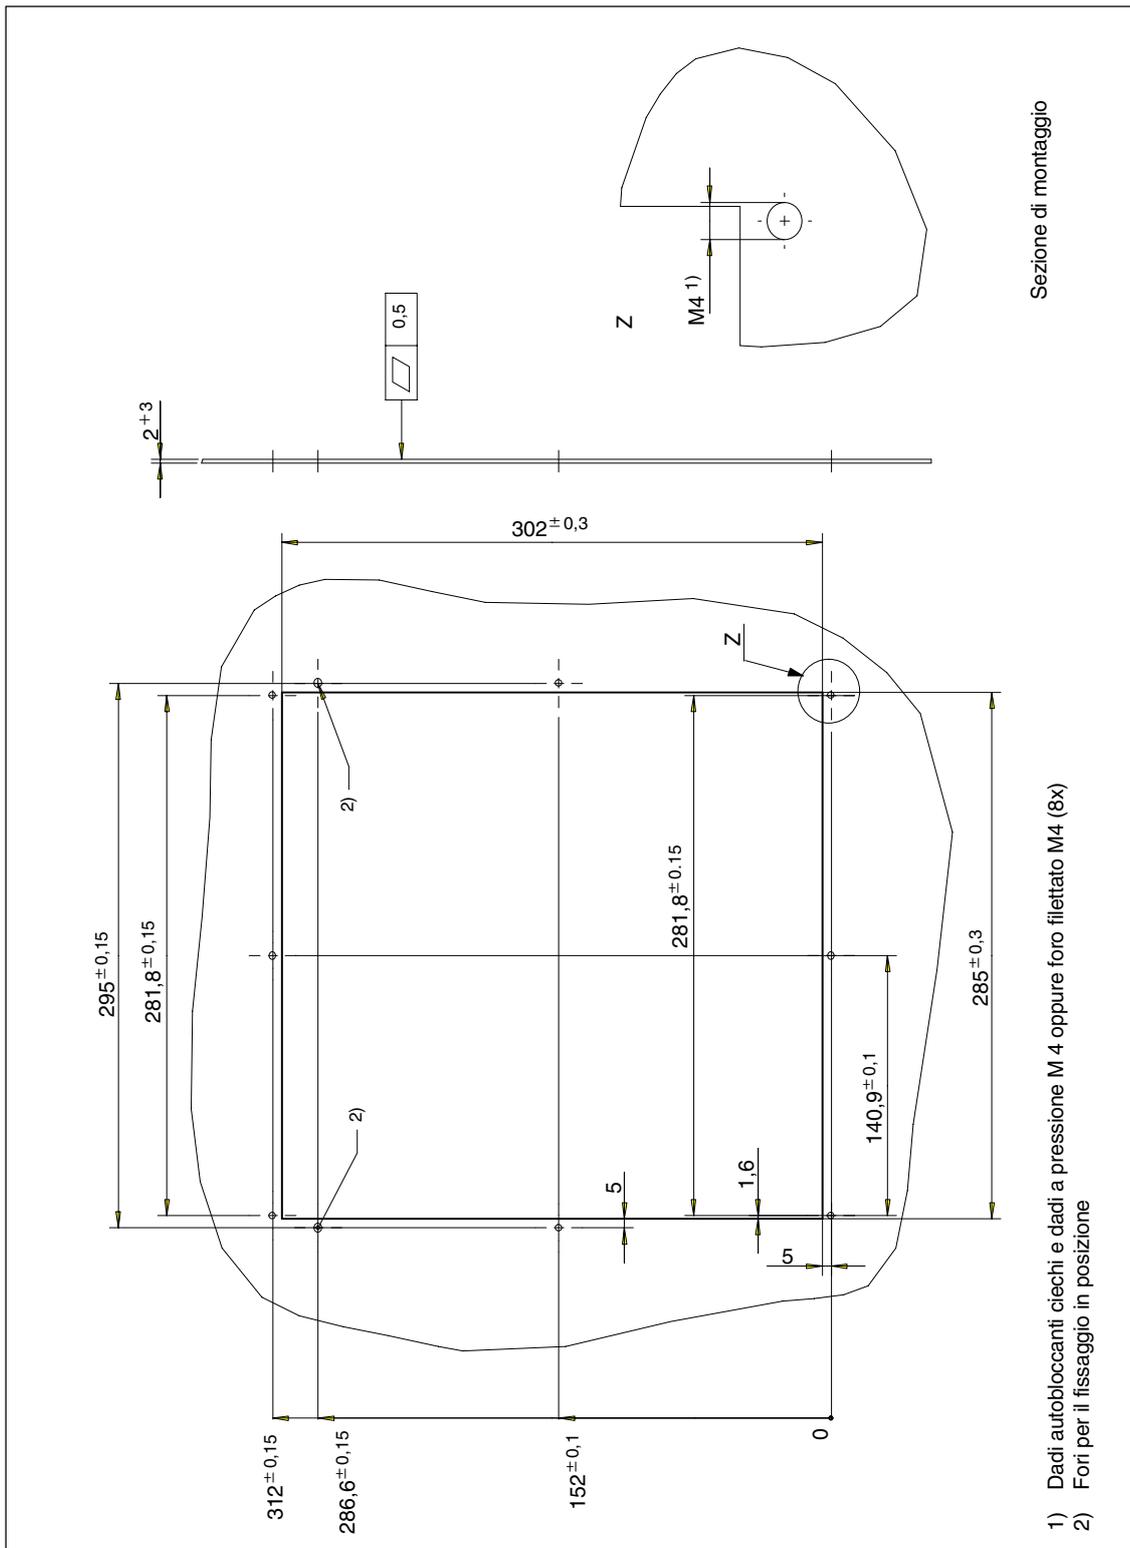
Schema di foratura per il pannello di servizio CNC
